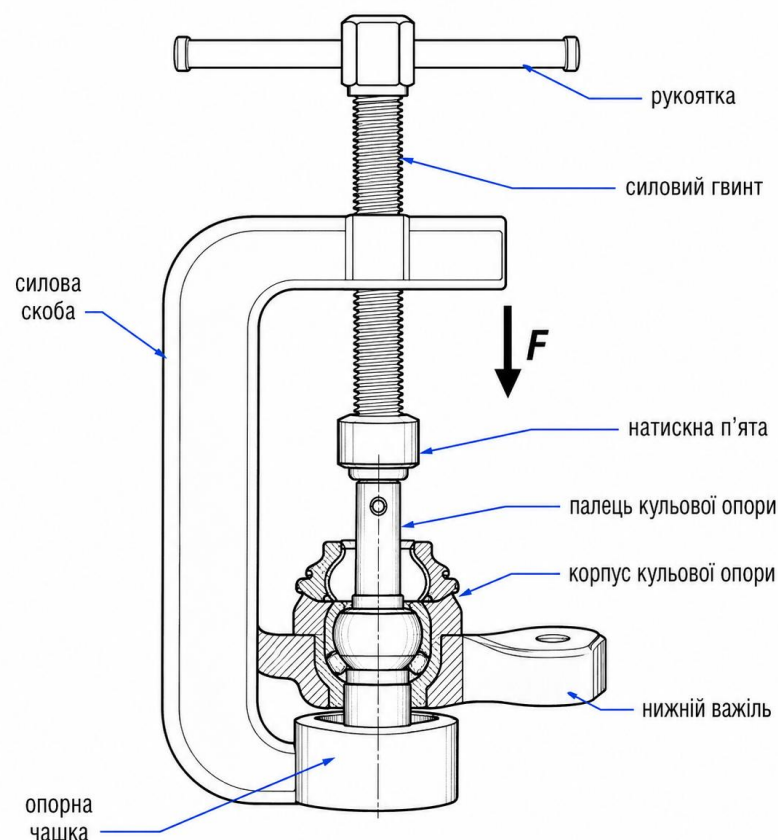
Загальна схема пристосування для випресування пальця кульової опори.
